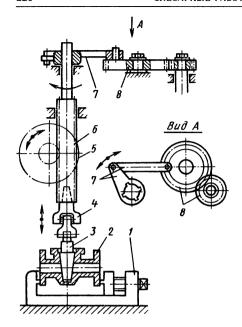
Приспособление для притирки пробковых кранов: 1 — тиски; 2 — кран; 3 — пробка; 4 — шарнир Гука; 5 — штурвал; 6 — шпиндель; 7 — кривошипно-шатунный механизм; 8 — шестерни
